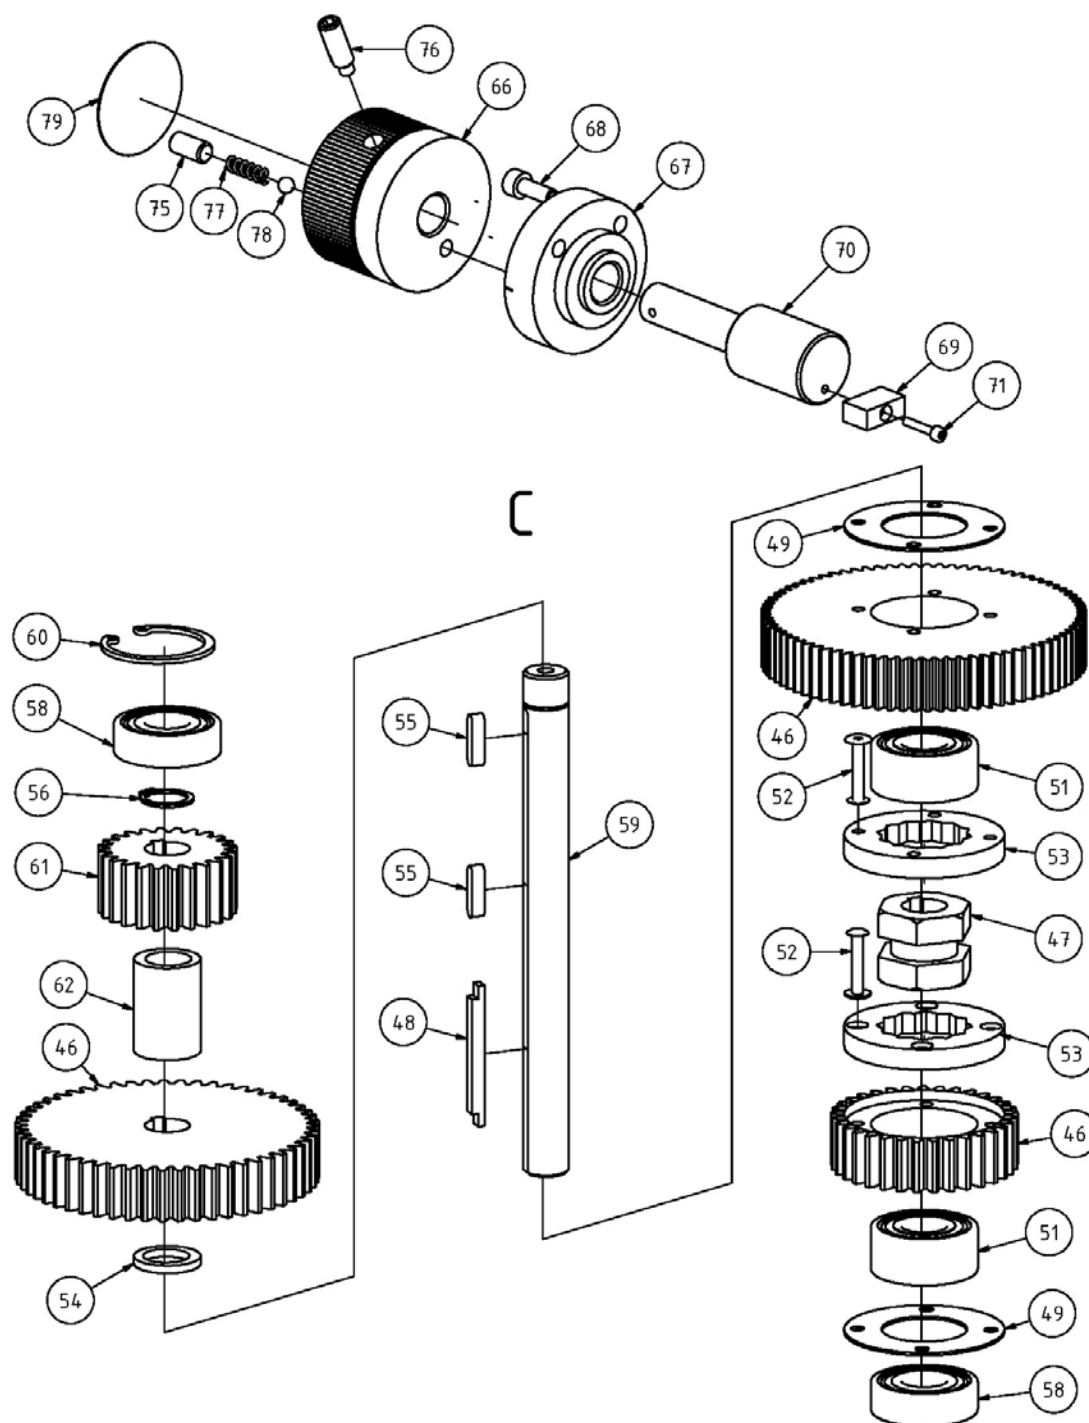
Bohrkopf 3 von 6 - Cabezal taladrador 3 de 6
